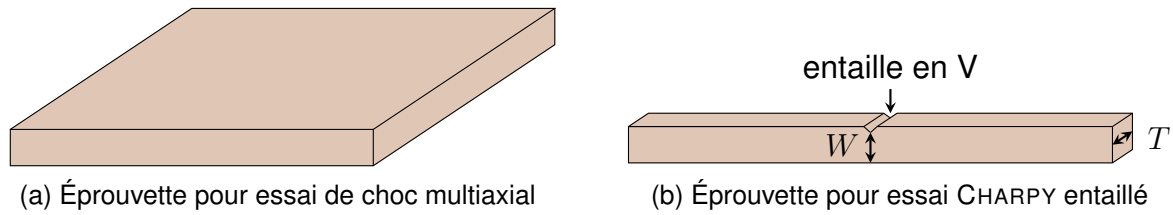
Éprouvette pour essai CHARPY entaillé
